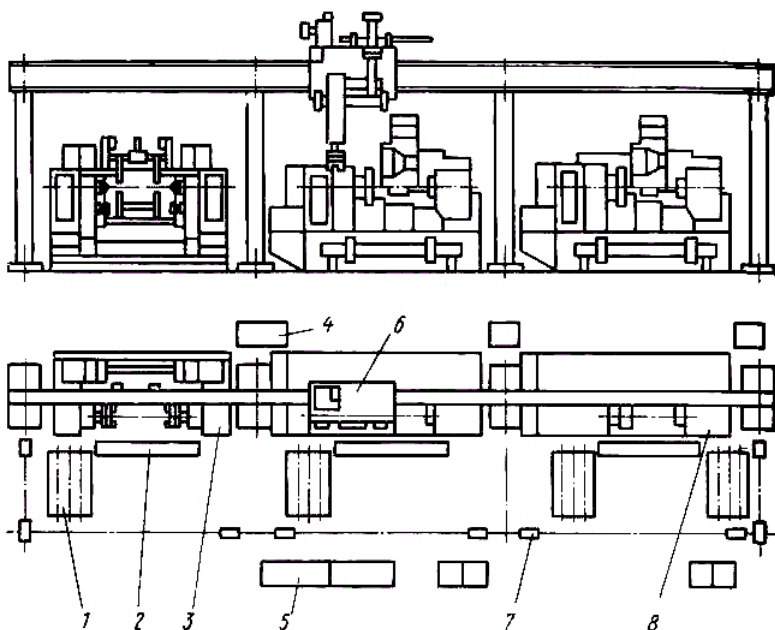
Планировка РТК мод.АСВР-01; 1- магазин, 2- промежуточная позиция, 3- фрезерно-центровальный станок мод.МР-179, 4- гидростанция ПР, 5- электрошкаф, 6- ПР мод.УМ160Ф2, 7- система светозащиты, 8- токарный станок с ЧПУ мод.1Б732Ф2.
